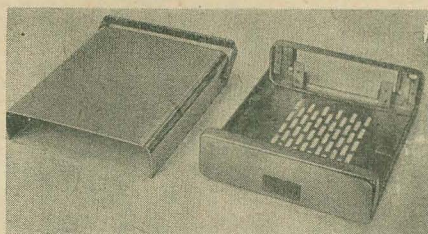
Empfangsteilgehäuse mit punktverschweißten Befestigungswinkeln
